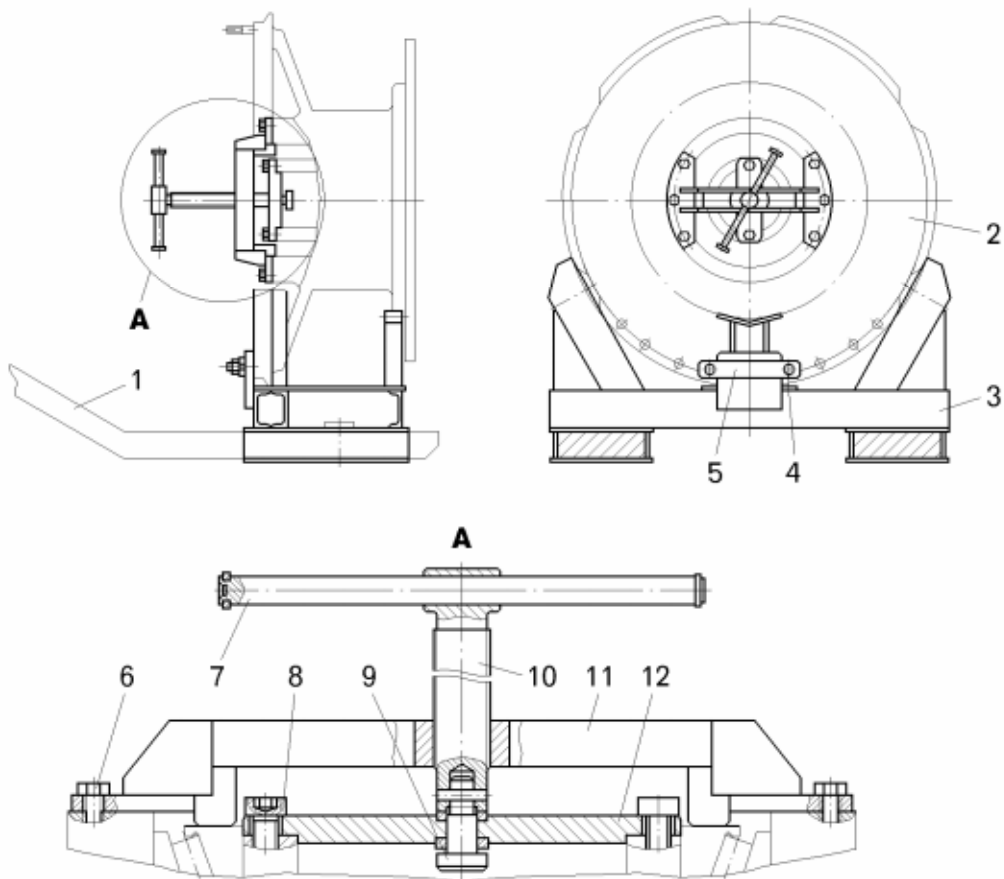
Приспособление для снятия и установки передней ступицы:
